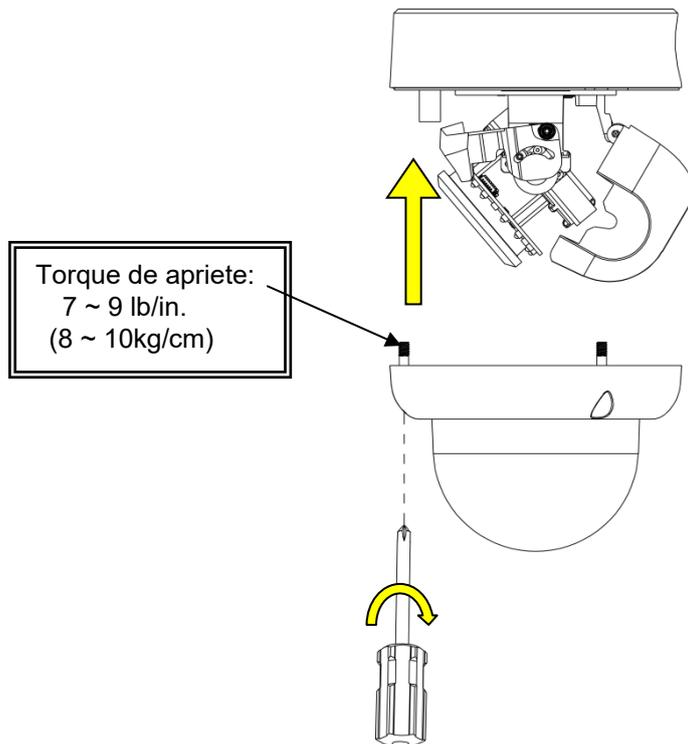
9: Montaje y finalización del montaje de la cámara
